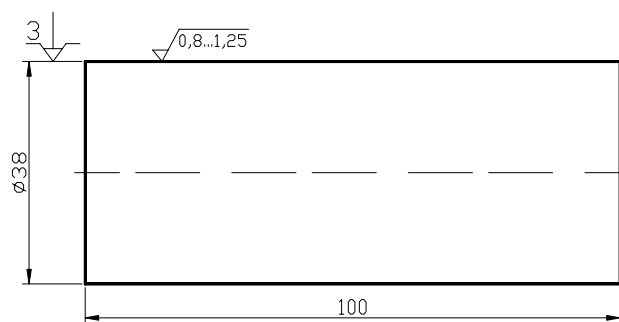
Заготовка – вал $\varnothing 38$ из стали У8А
